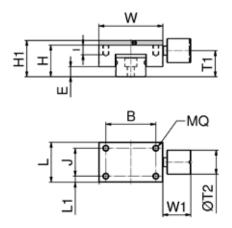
Manuelle Klemmelemente für Miniaturführungen
